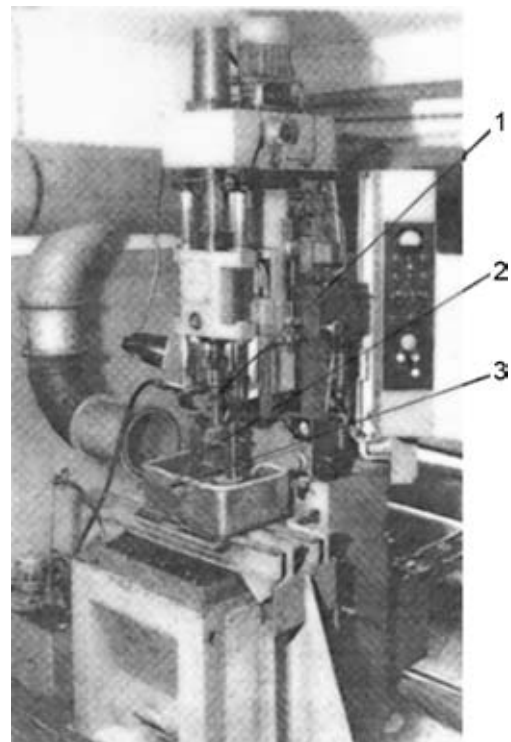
Общий вид установки: 1 — хонголка "плавающего" типа; 2 — установочное приспособление с опытным образцом детали; 3 — двухкомпонентный тензометрический динамометр
